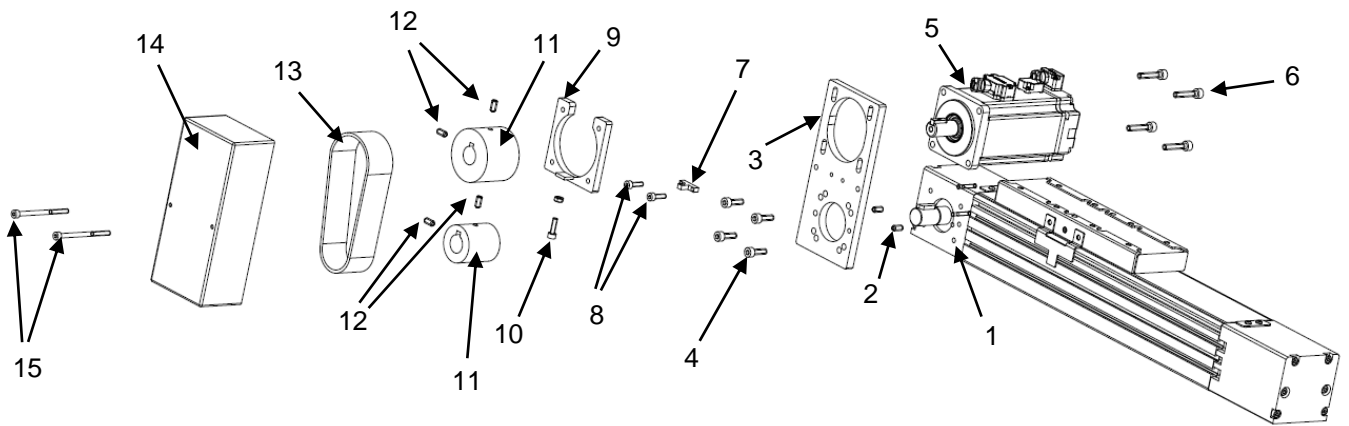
Установка двигателя/редуктора с помощью монтажного комплекта модели PM-MKCR
